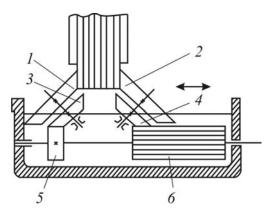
Клеевой аппарат для боковой промазки: 1, 2 – конические диски; 3, 4 – конические колеса; 5, 6 – зубчатые колеса
